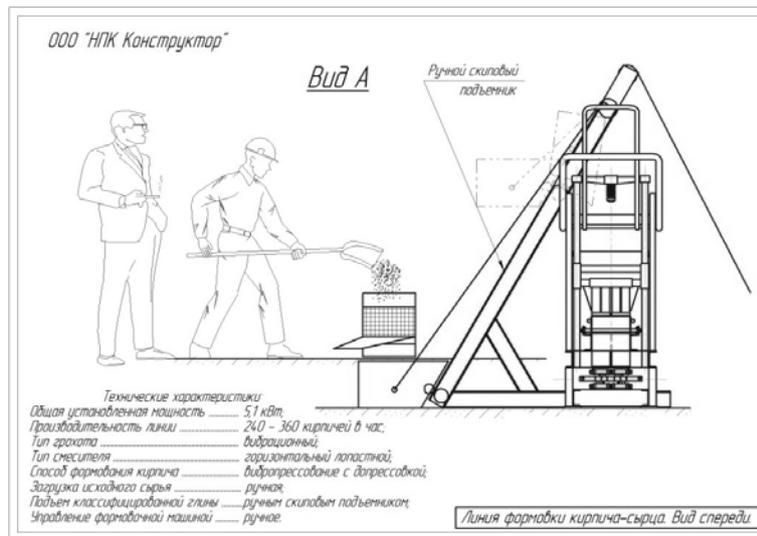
Линия формовки кирпича-сырца. Вид спереди
